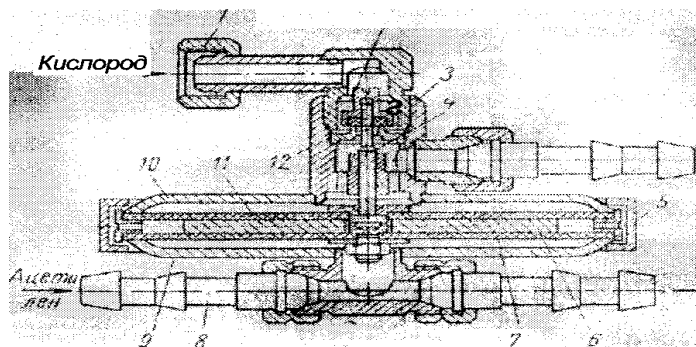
Схема беспружинного регулятора равного давления ДКР-1-56:
